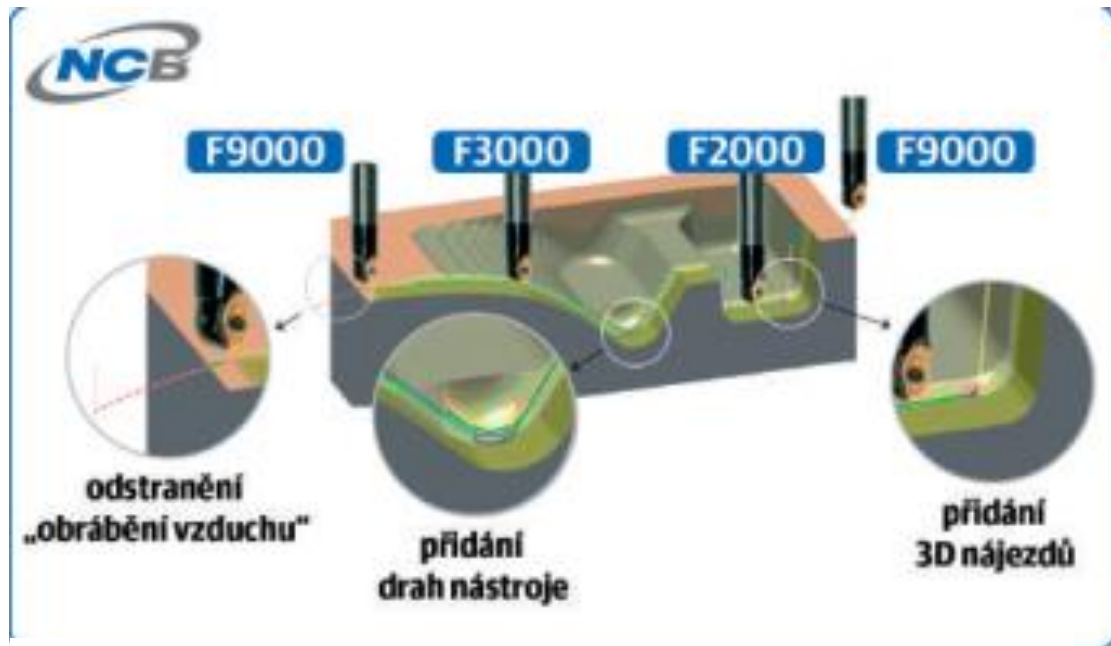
Optimalizace posuvu - OPTITOOL [29]
